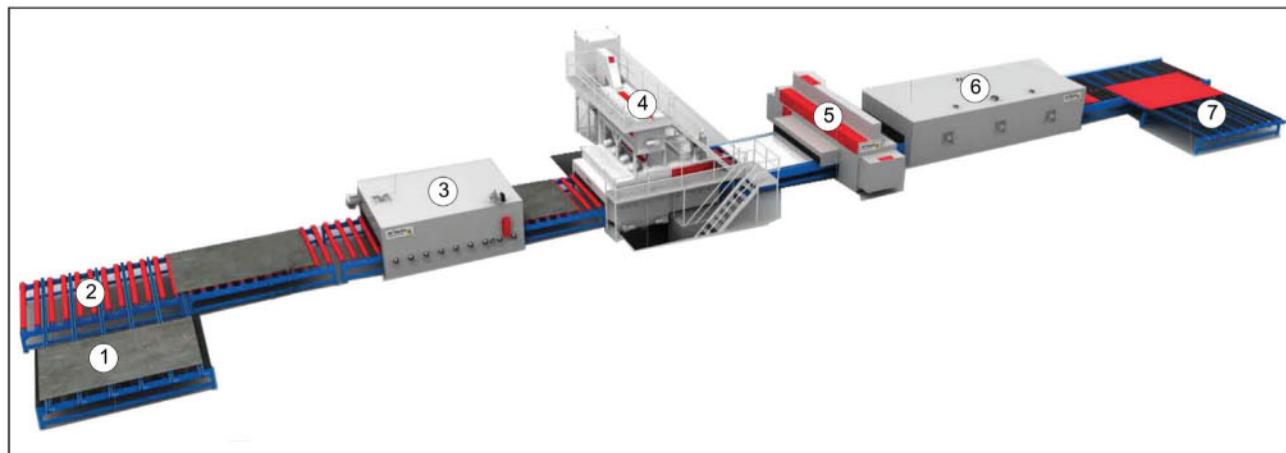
Линия дробеметной очистки и грунтовки листового и профильного проката: 1 — загрузочный конвейер; 2 — транспортная система; 3 — камера сушки и нагрева; 4 — дробеметная камера; 5 — камера грунтовки; 6 — камера сушки; 7 — принимающий конвейер
